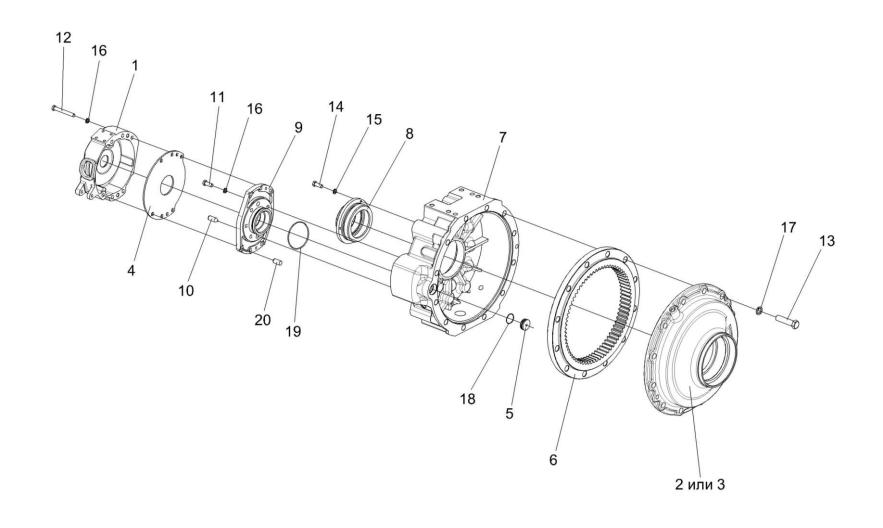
Редуктор правый МК-23М.04.000-03 (корпус, крышки)
